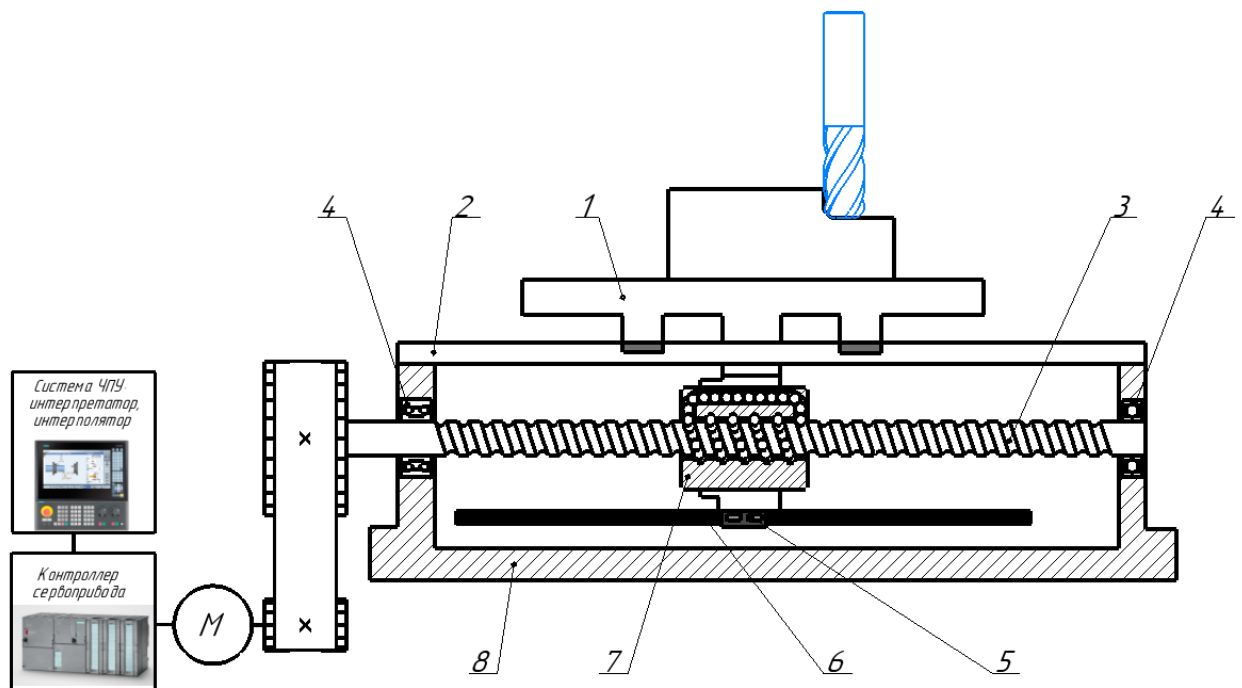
Общая схема привода с шарико-винтовой передачей в процессе фрезерования
